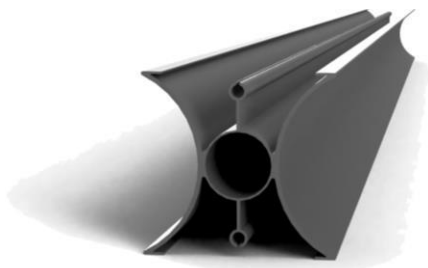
Инфракрасный излучающий профиль марки Helios 750
